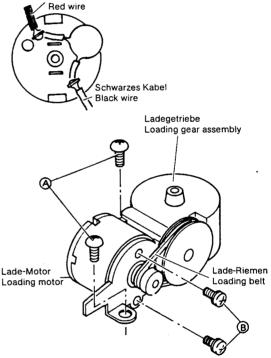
Lade-Motor tauschen Fig. 3-8 Loading motor replacement
